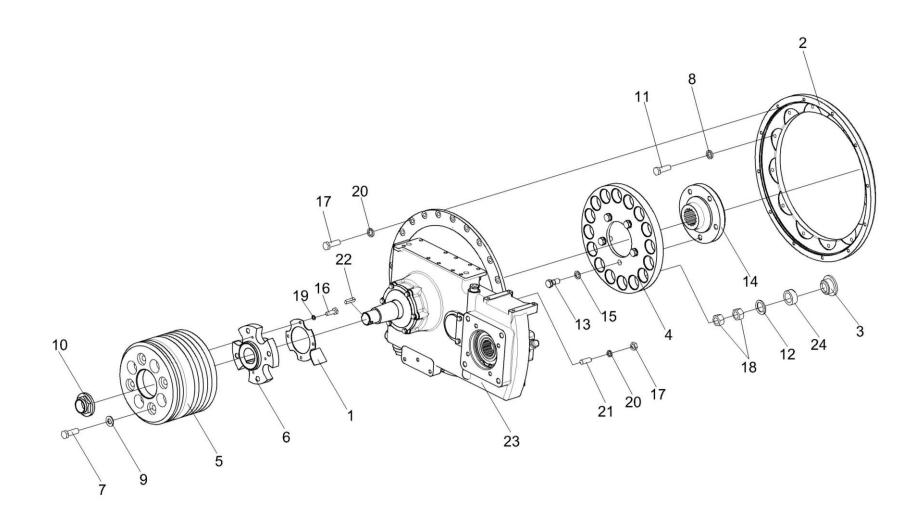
Установка главного привода КЗК-10-1-0106030
